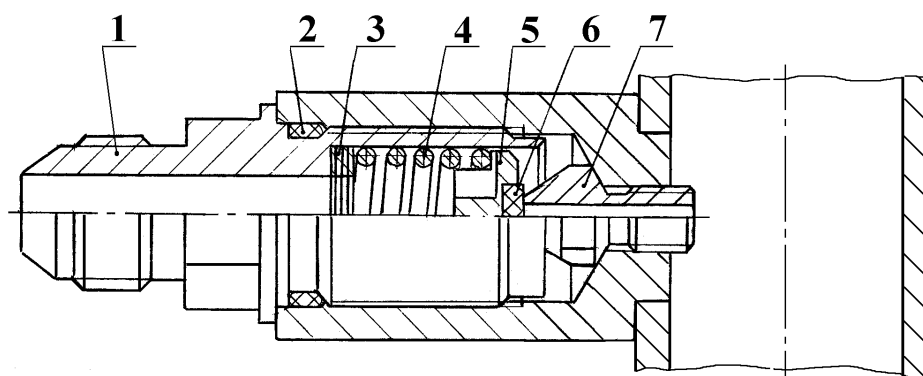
Клапан перепускной насоса НЦПК-40/100-4/400: 1 — штуцер; 2 — кольцо уплотнительное; 3 — прокладки регулировочные; 4 — пружина; 5 - клапан; 6 — прокладка уплотнительная; 7 - втулка
